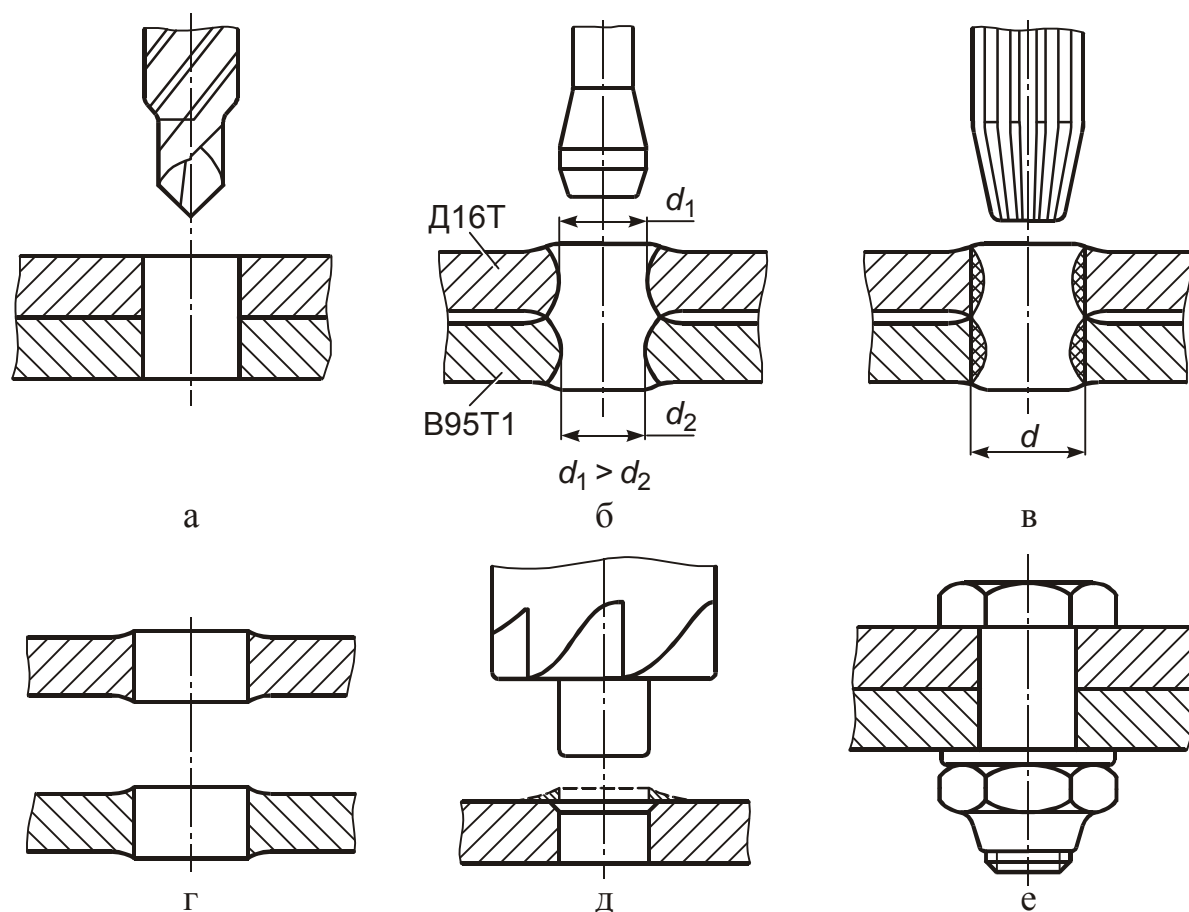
Технологический процесс выполнения высокоресурсного соединения: а – сверление ступенчатым сверлом; б – дорнование отверстий однозубым дорном с натягом 1,3...4,0%; в – калибрование отверстий разверткой; г – разборка пакета; д – снятие наплывов; е – окончательная сборка болтового соединения
